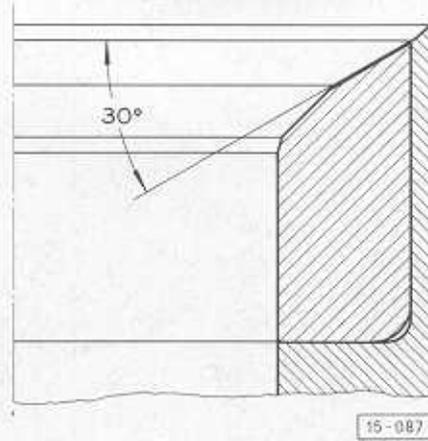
30°-Sitzfläche bearbeiten – Einlaßventil
